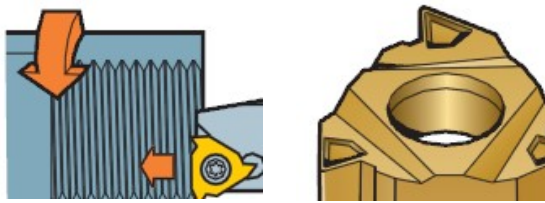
Інструмент для нарізання внутрішнього різьблення
